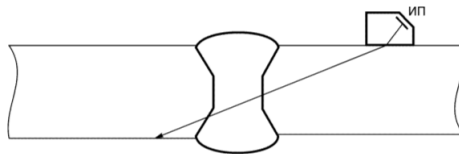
Схема прозвучивания стыкового сварного соединения прямым лучом
